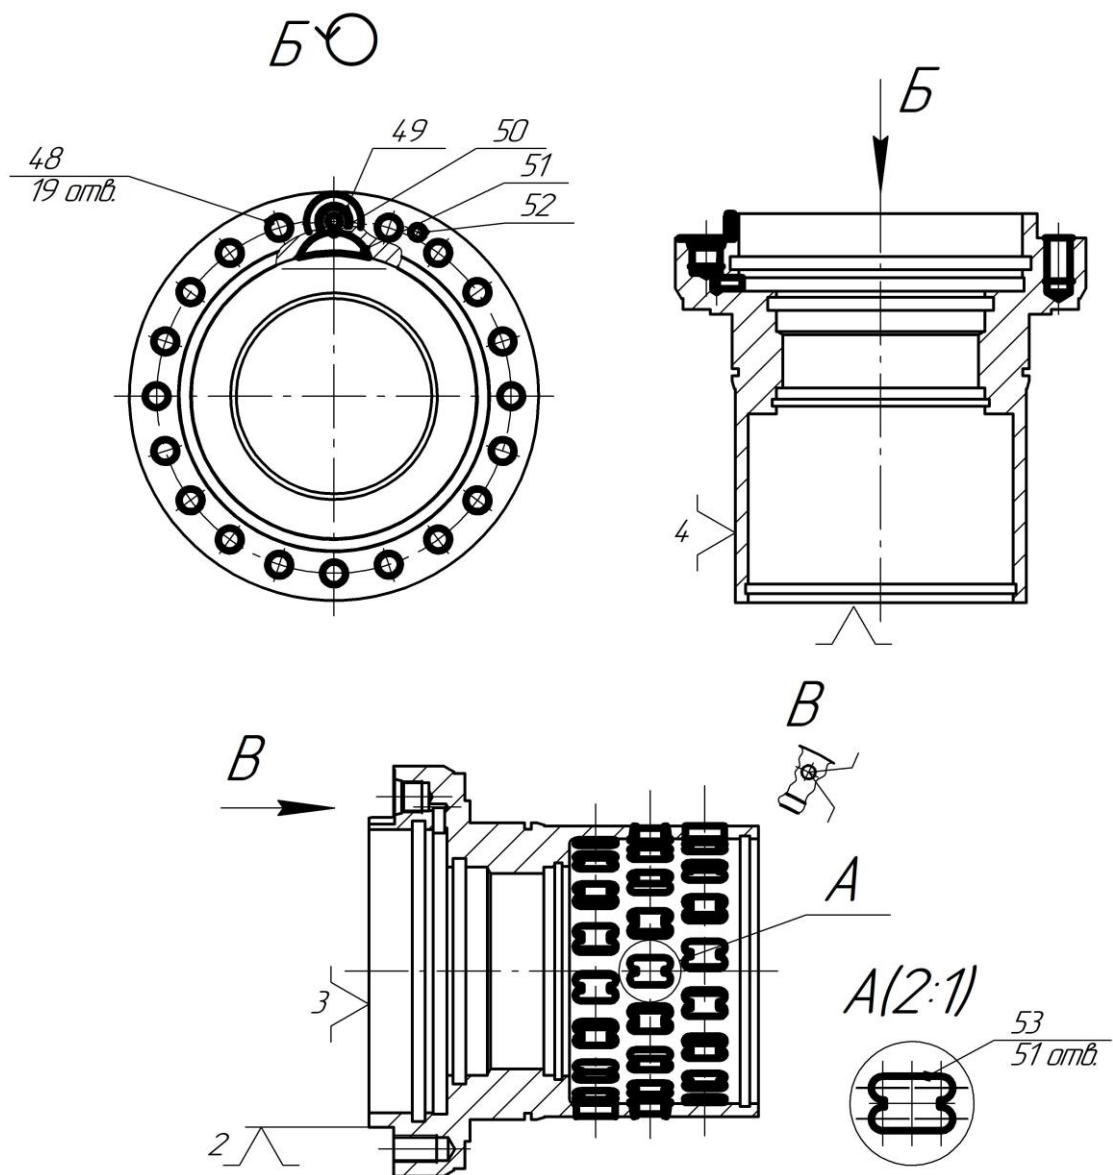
Эскиз фрезерной операции с ЦПУ
